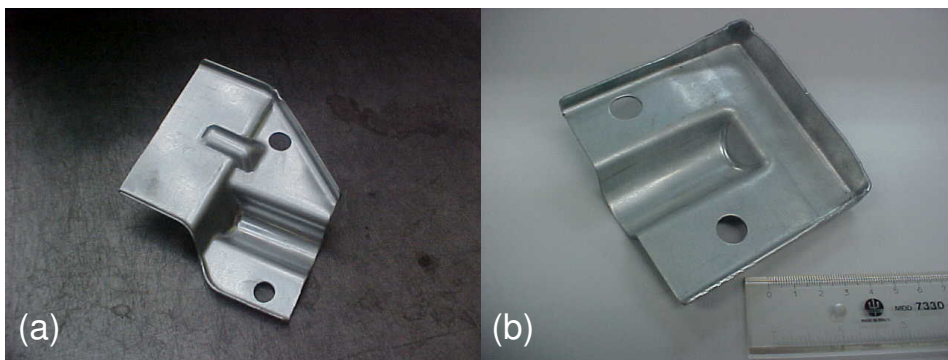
(a – b) Suportes estampados que posteriormente são soldados nas extremidades das barras tubulares
